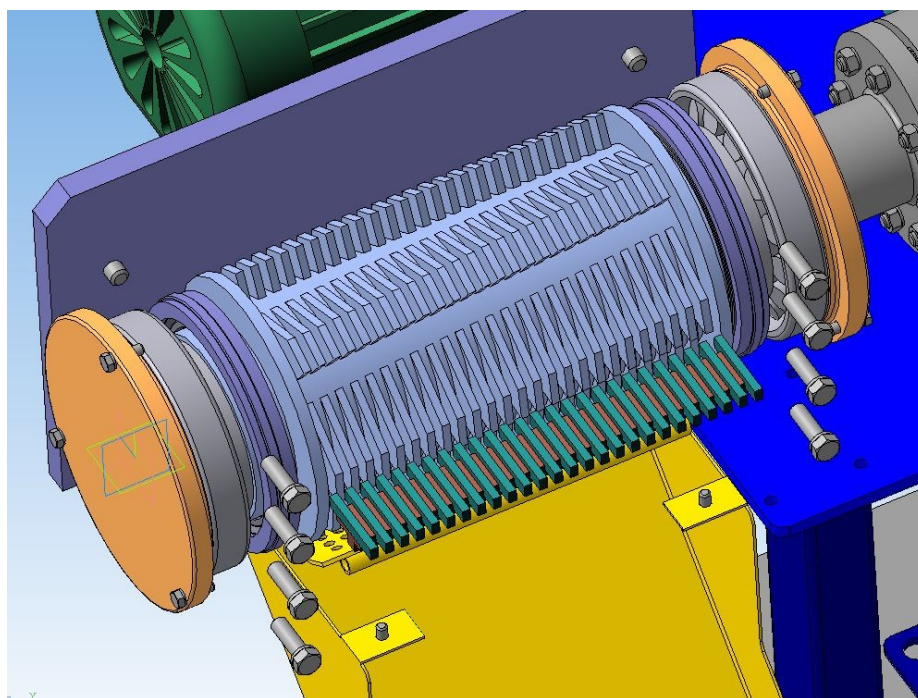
Внешний вид режущего ротора одновалкового шредера
